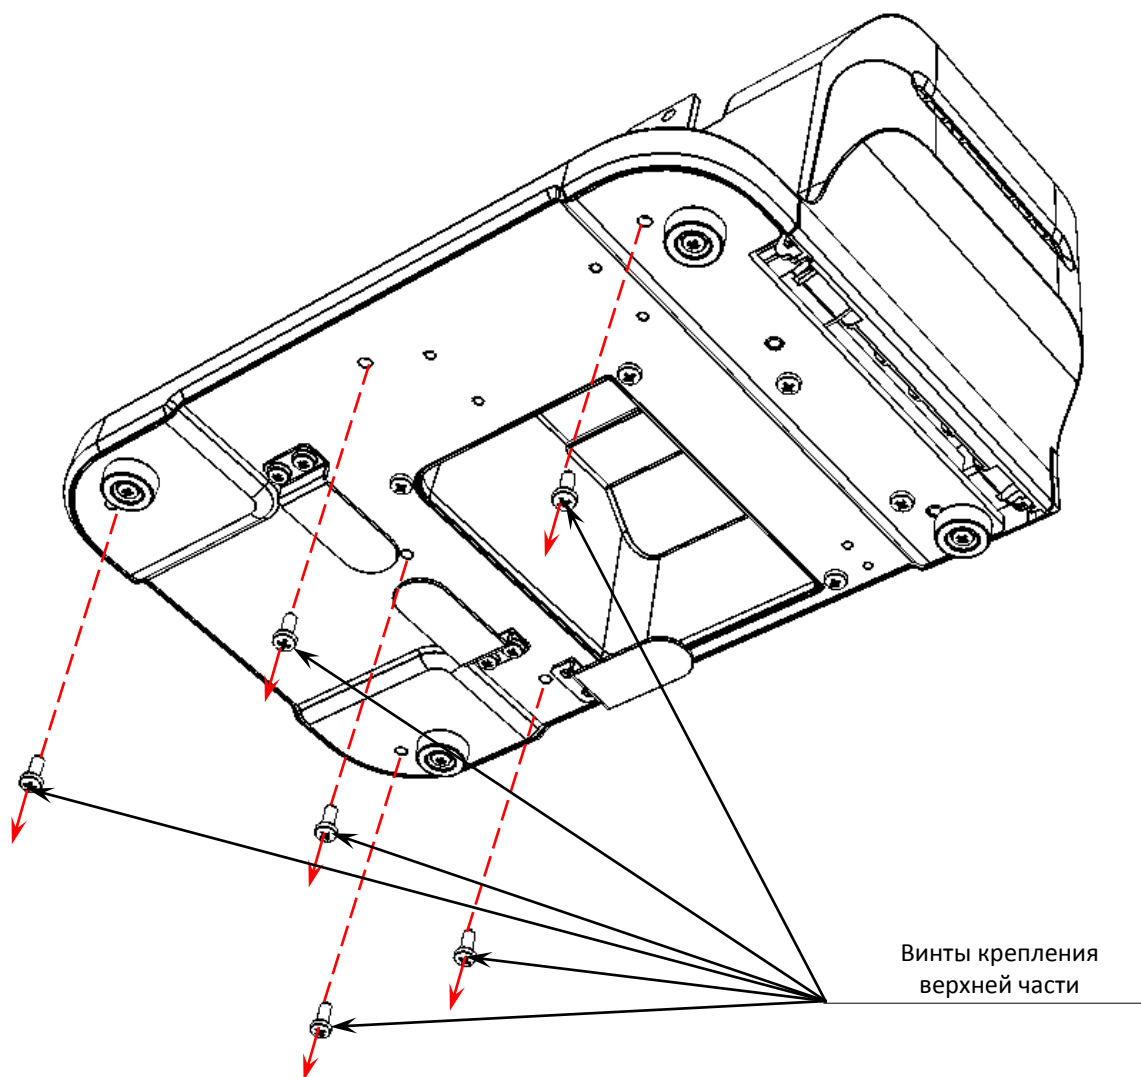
Винты крепления верхней части к дну корпуса ККТ
